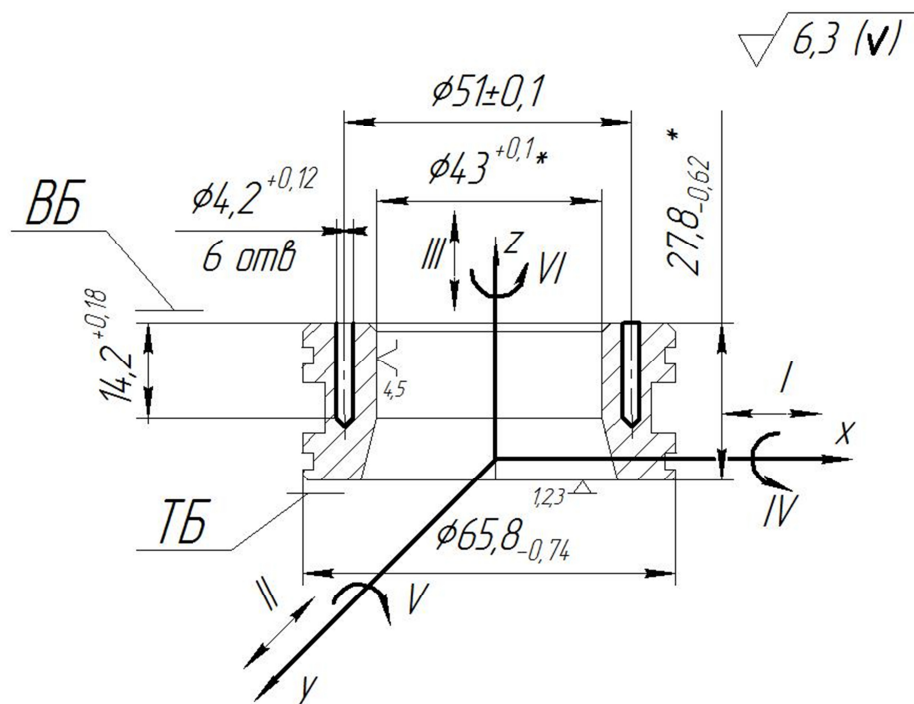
Схема базування заготовки на операції 035 Свердлувальна з ЧПК
